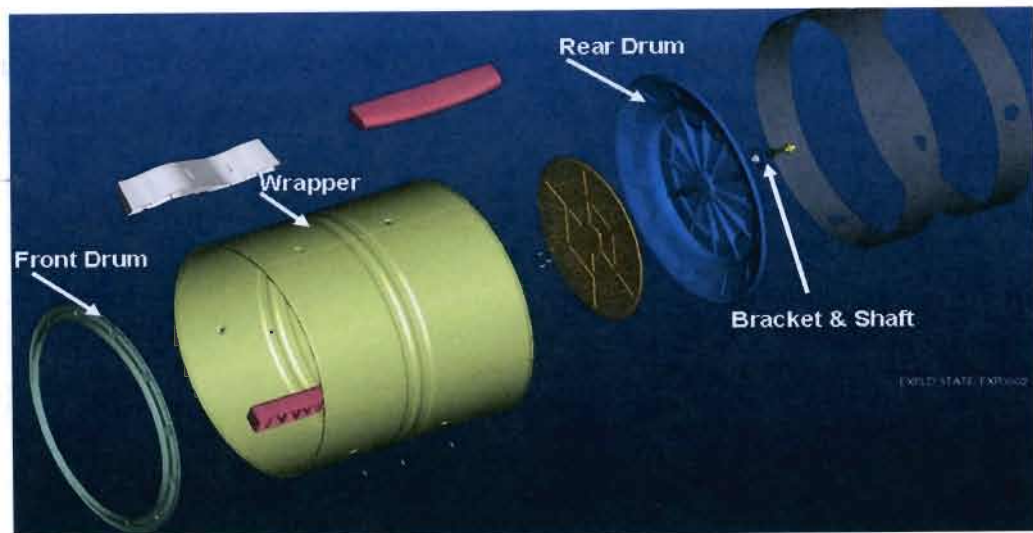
Explosionado de Partes que Componen el Tambor.
